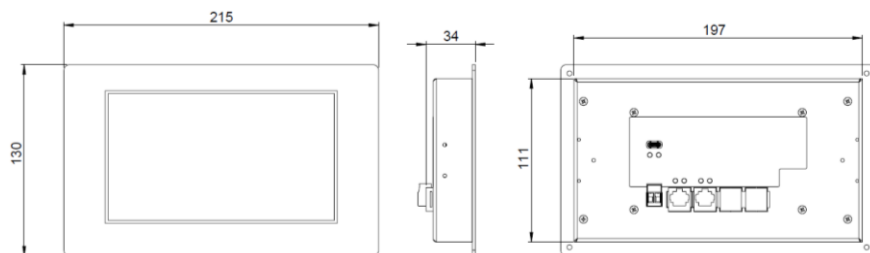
Dimensões do Equipamento MASTERVIEW 7”.
